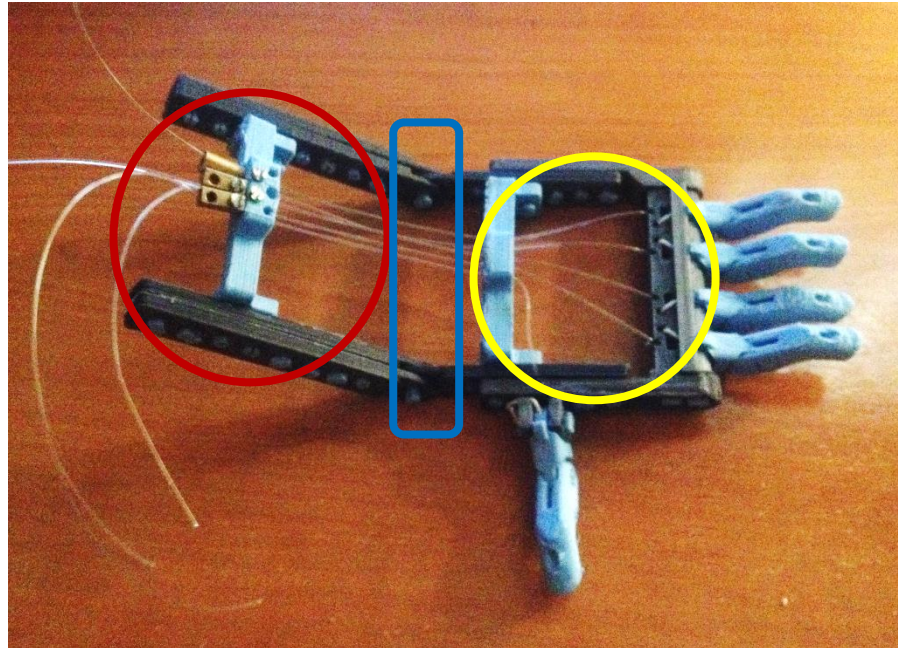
Prótesis Snap-Together Robohand fabricada
